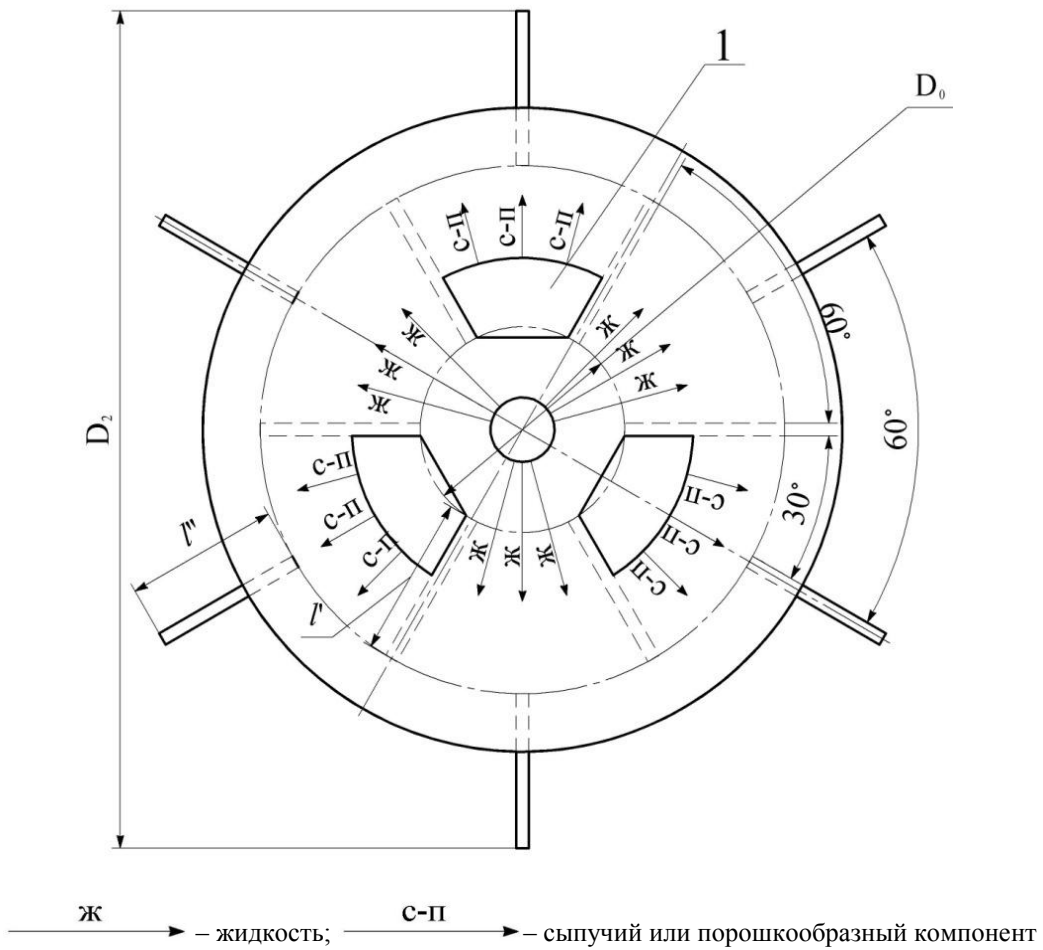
Схема рабочего колеса установки для приготовления смесей
